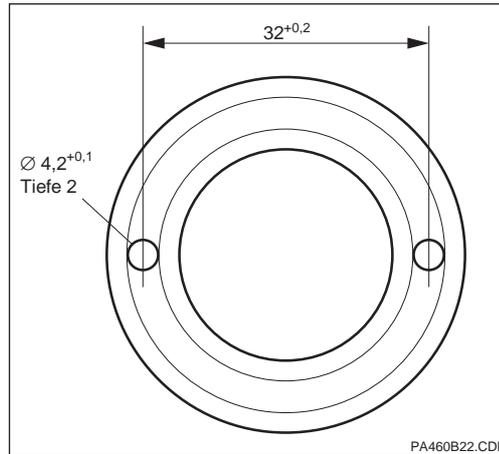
Draufsicht auf Einbauadapter DN 25
